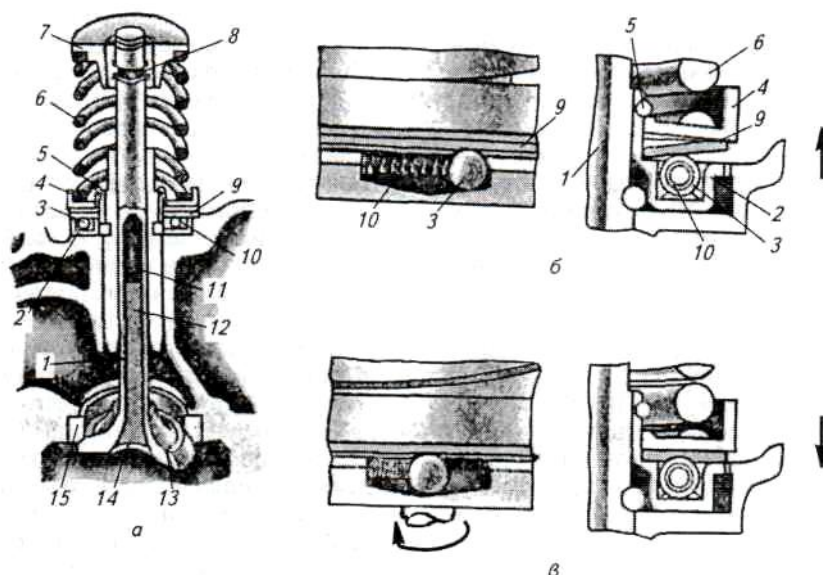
Выпускной клапан в сборе механизма газораспределения двигателя ЗИЛ:
